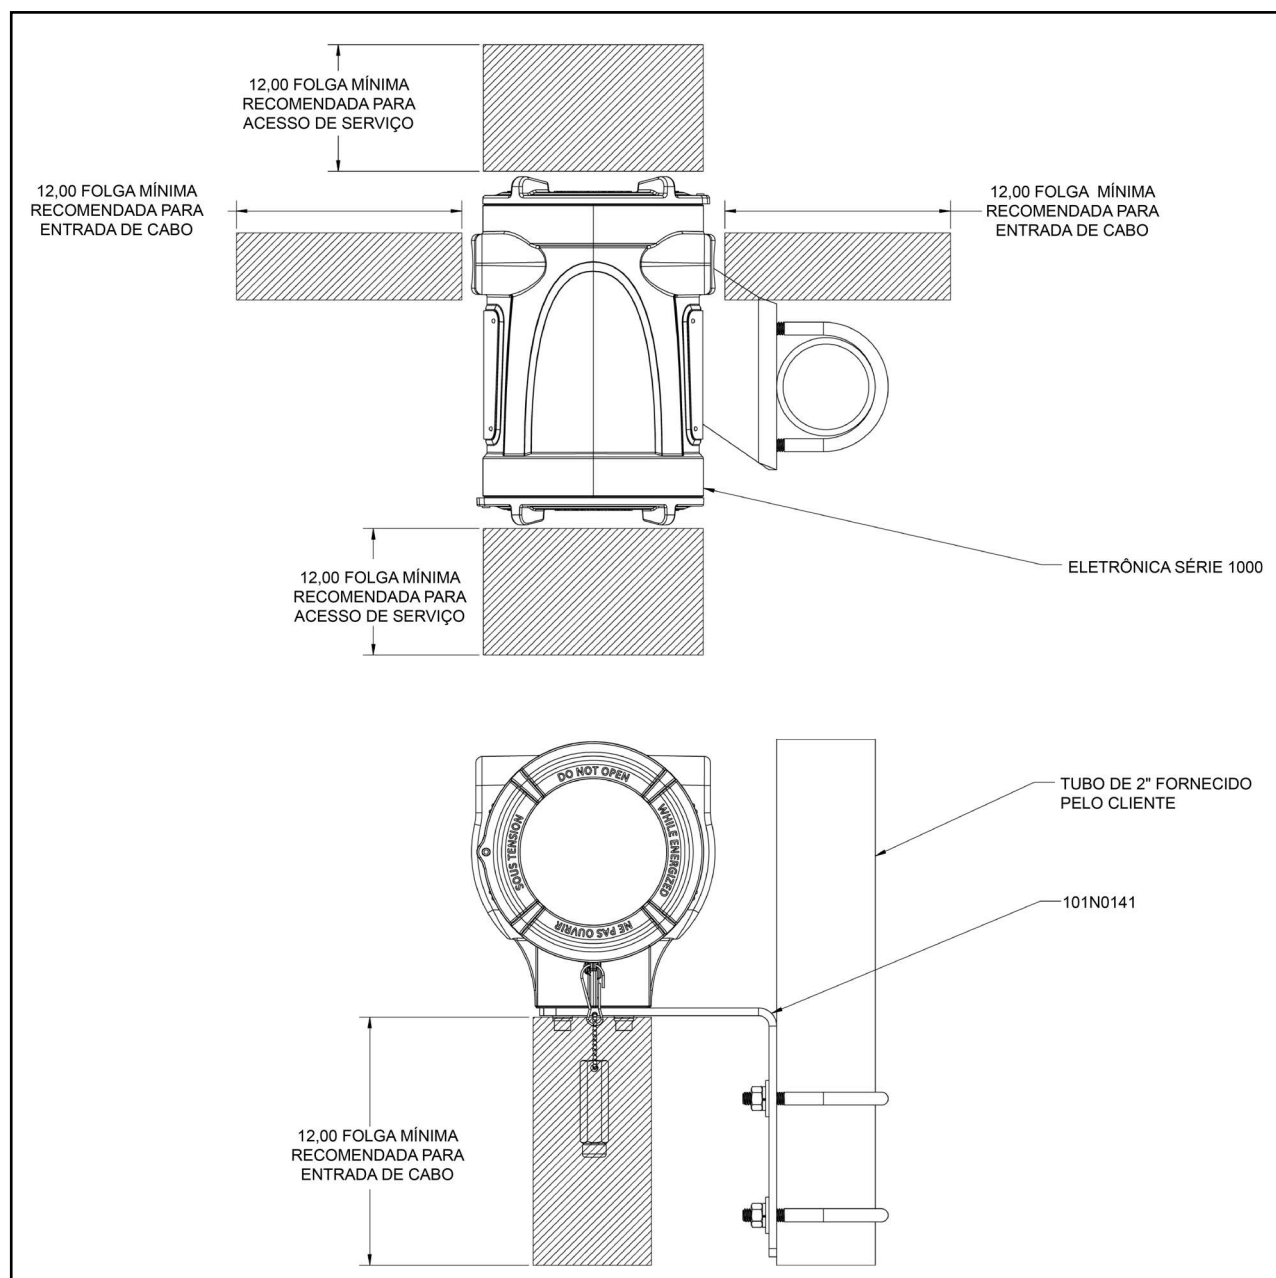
Folgas do Invólucro XMT1000 (ref. desenho 712-2164)
